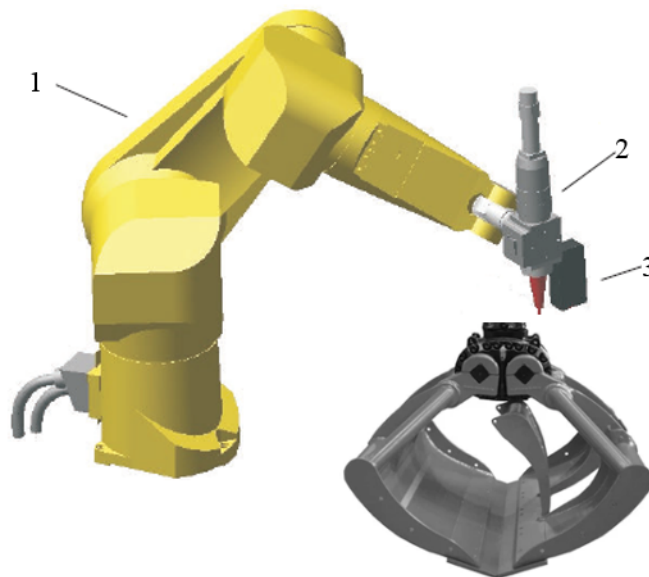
Схема одержання зварного грейфера: 1 – робот; 2 – зварювальна головка; 3 – сенсор аналізу поверхні.
